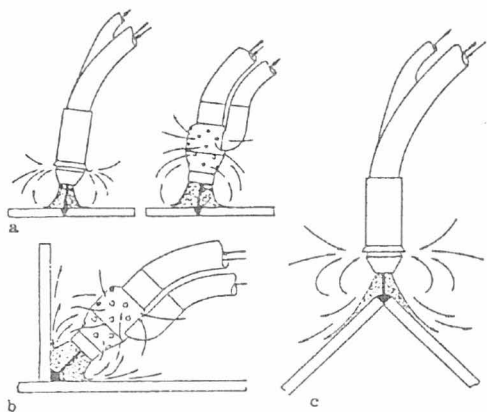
Odsávání svářecích zplodin polootevřenou kabinou
